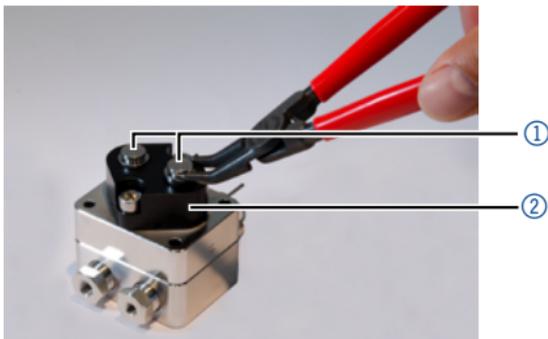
Entfernen der Kolbenstangen aus der Kolbenführung
